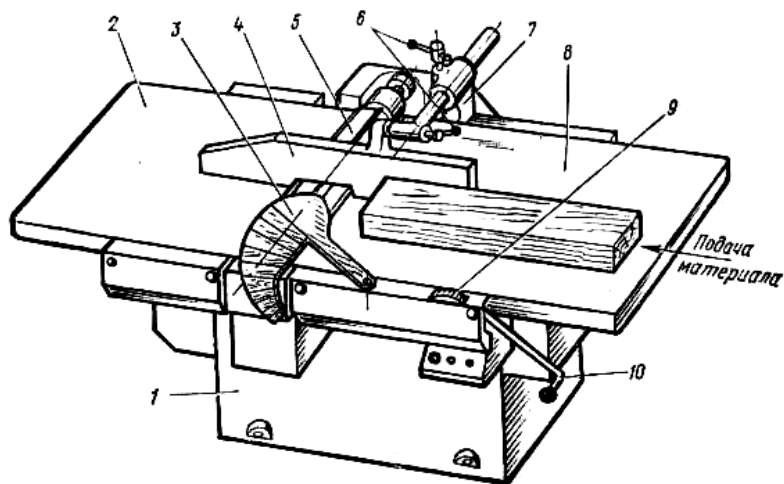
Одношпиндельный фуговальный станок СФ6-1:
